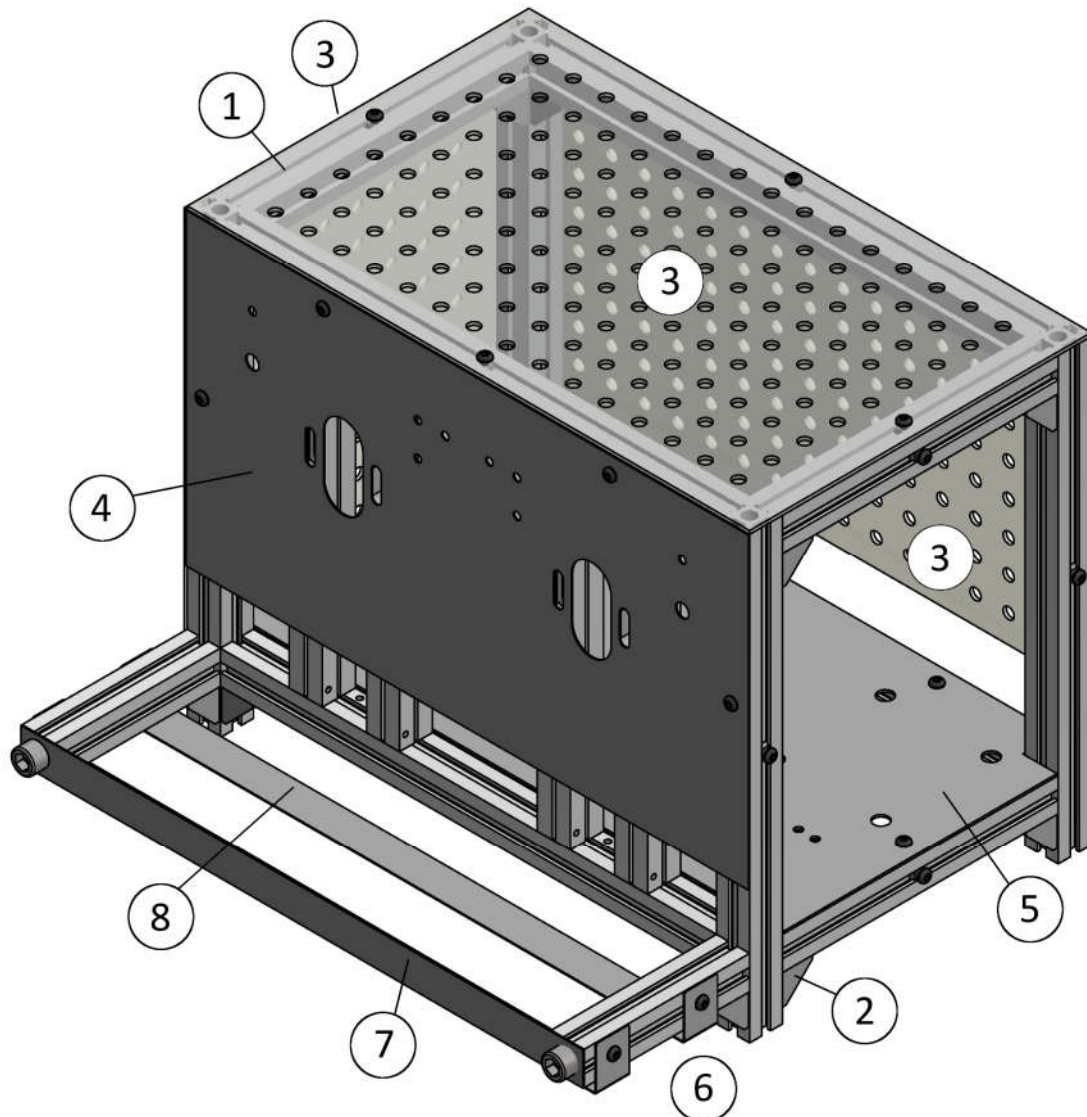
Mechanisches Grundgerüst der labortechnischen espressomaschine
